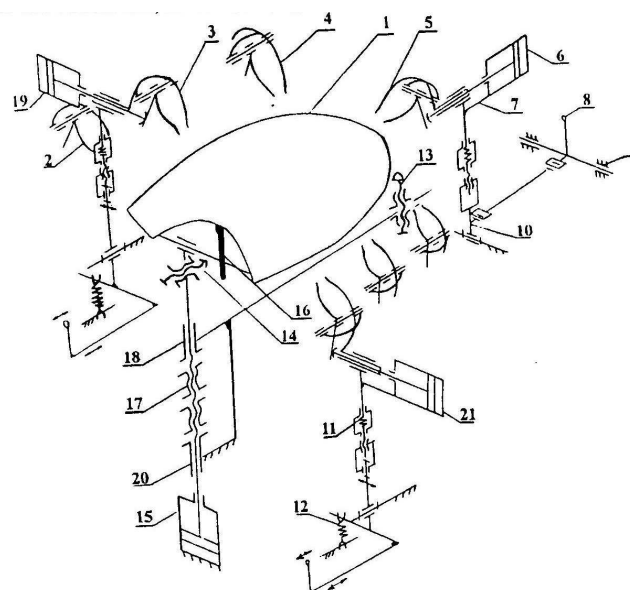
Кинематическая схема машины для формования носочно-пучковой части заготовки верха обуви
